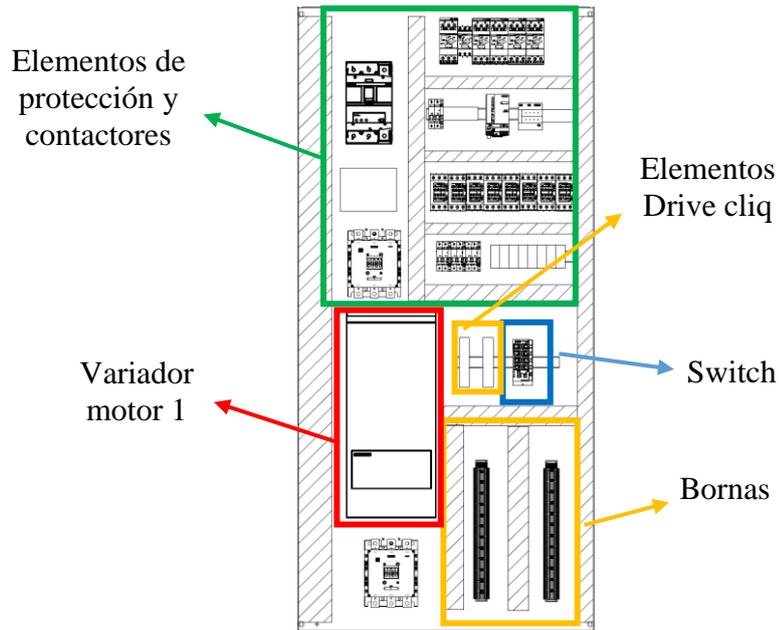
Placa de la Translación del Carro Auxiliar
